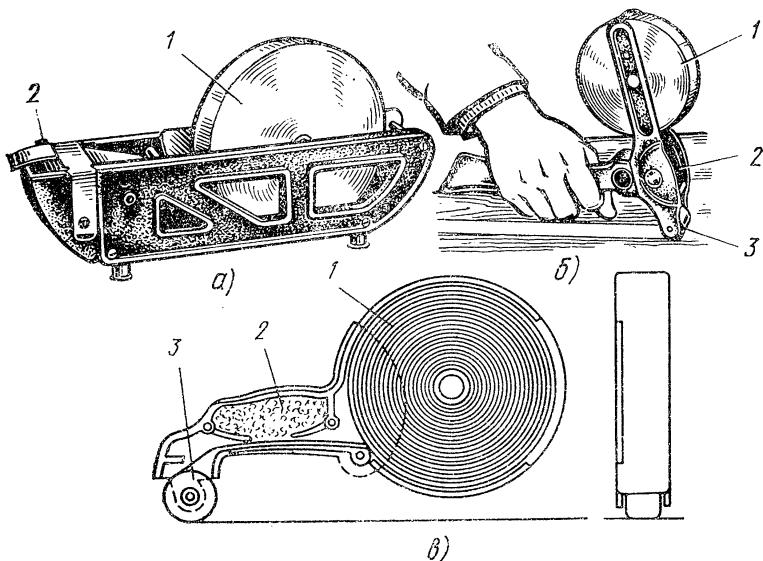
Приспособления для установки бобины kleевой ленты (а) и для наклеивания kleевой ленты (б, в):
